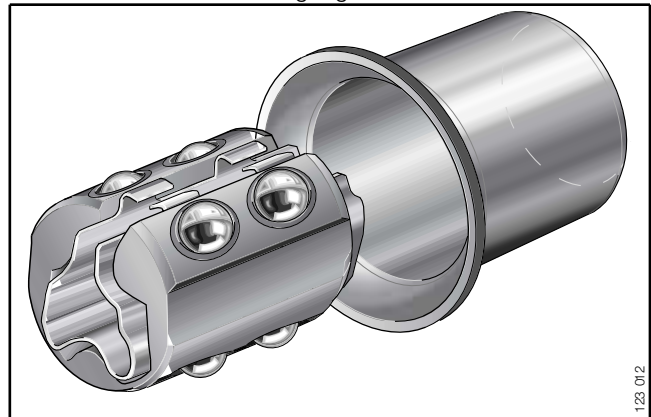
· Wälzlager für begrenzte Längsbewegung und für Schaltschienen mit rechteckigem Querschnitt
